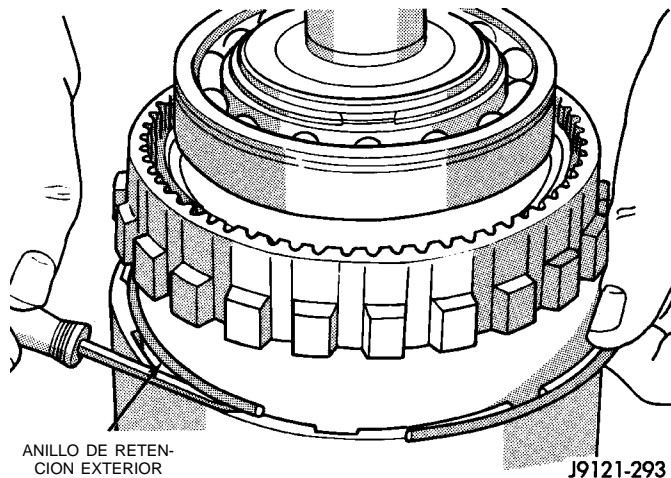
Desmontaje del anillo de retención exterior del tambor de embrague
